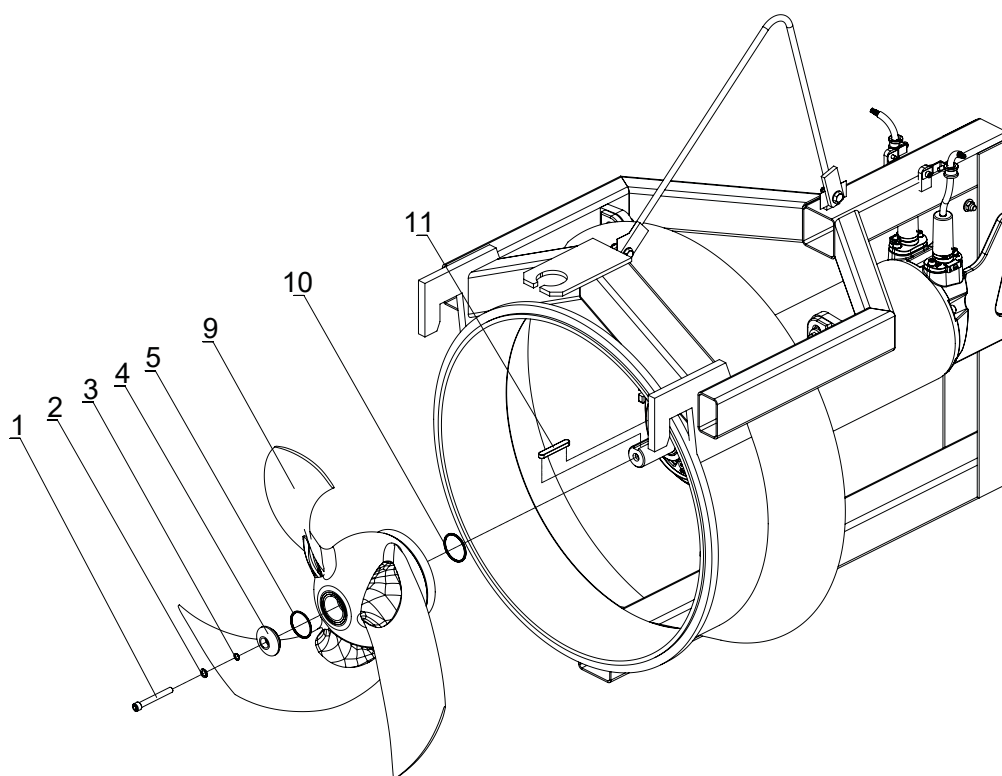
Rotor montage / demontage XRCP 400/500
